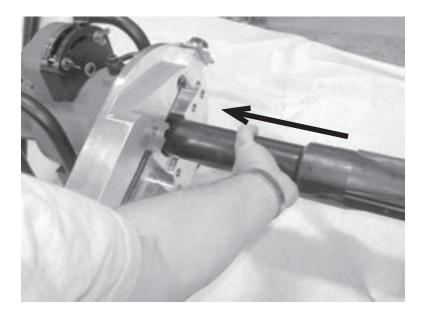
Tirez sur le mandrin pour le sortir de la machine.
